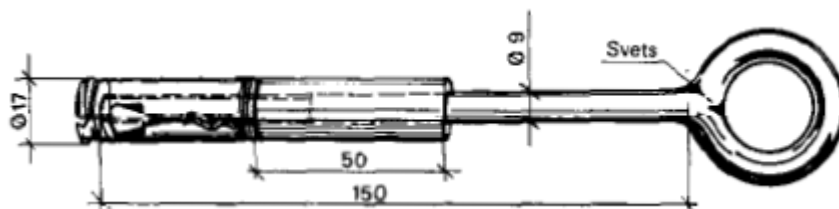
3/8" expander. Borrhål i vägg \varnothing 18 mm. Borrdjup 100 mm.
